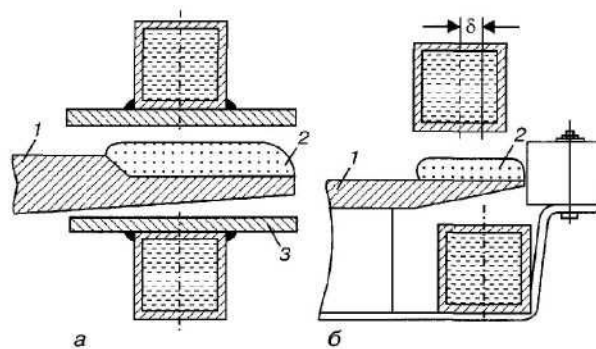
Схема розташування при наплавленні лемеша (а) і лапи культиватора (б):
